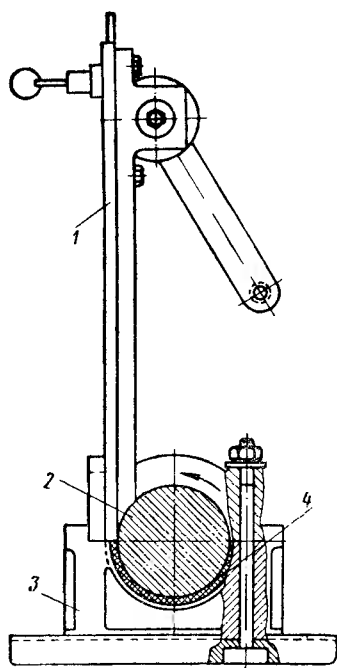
Приспособление для запрессовки сальника в держатель сальника:
